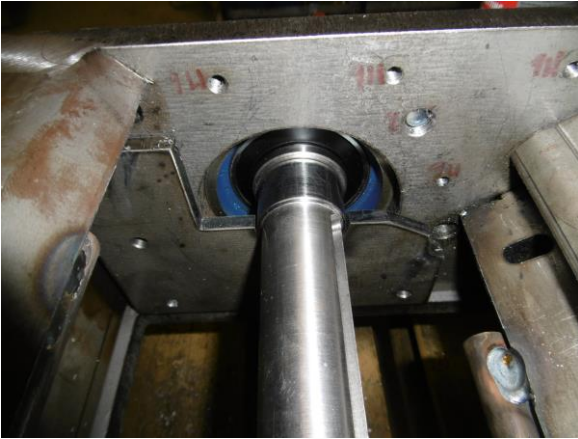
Maschine mit Welle und unterer Schleißplatte
